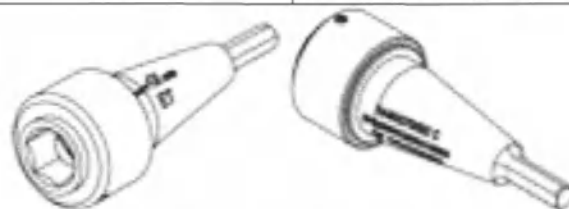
Адаптер для держателя фрез / Figure 48. Reamer adapter
